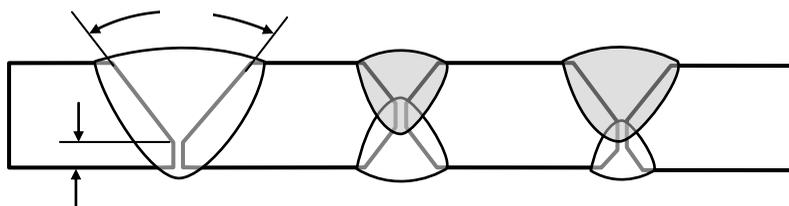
Форма разделки кромок, применяемая для ручной дуговой сварки
